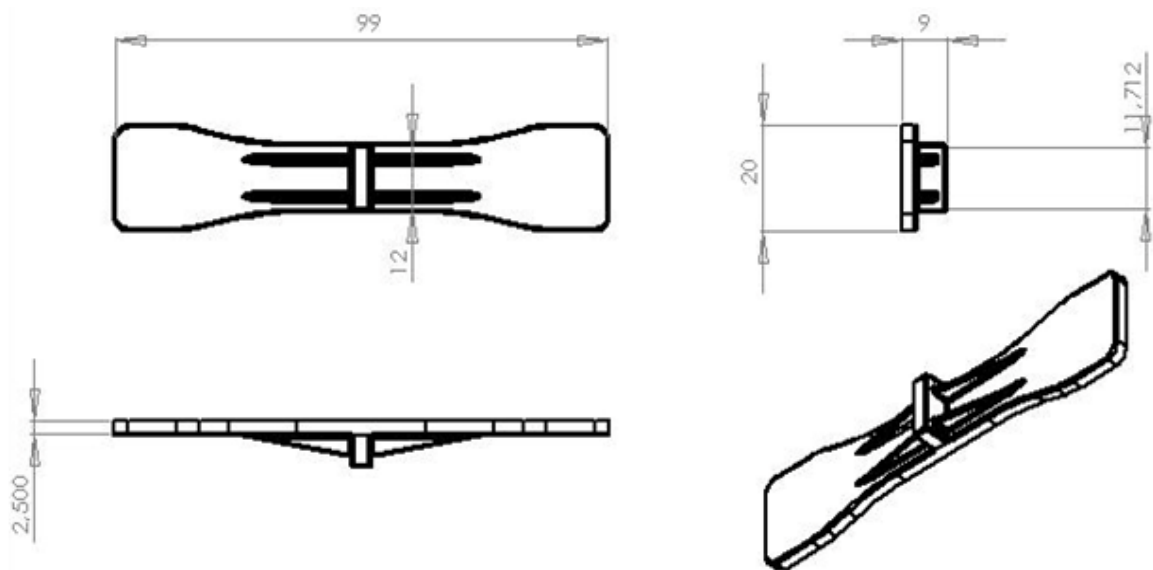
Representação esquemática bidimensional do corpo de prova para ensaios de tração.
